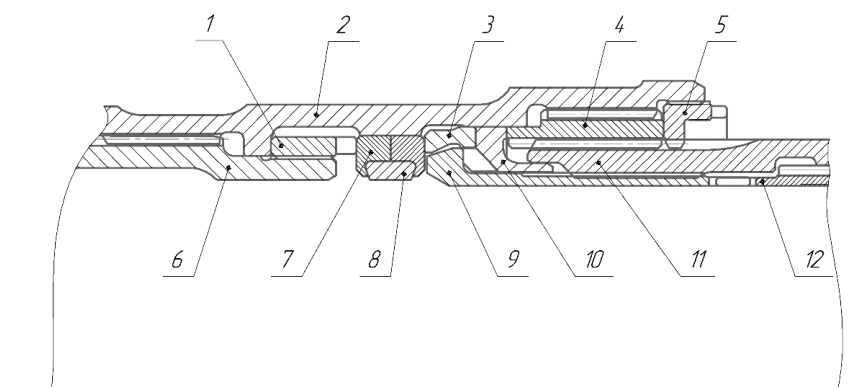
Место соединения роторов КВД и ТВД: 1 – гайка вала КВД; 2 – вал привода КВД; 3 – кольцо контролочное; 4 – втулка соединительная (штицевая); 5 – гайка вала привода; 6 – вал КВД; 7 – обойма; 8 – Втулка; 9 – втулка стяжная; 10 – кольцо сферическое; 11 – вал ТВД; 12 – втулка контролочная
